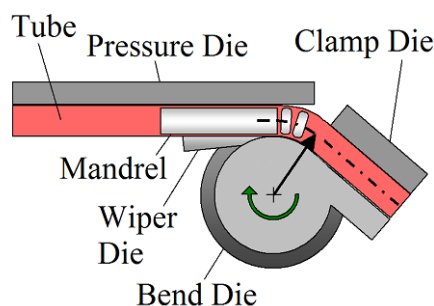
schematizzazione del processo di piego-stiratura (draw bending).
